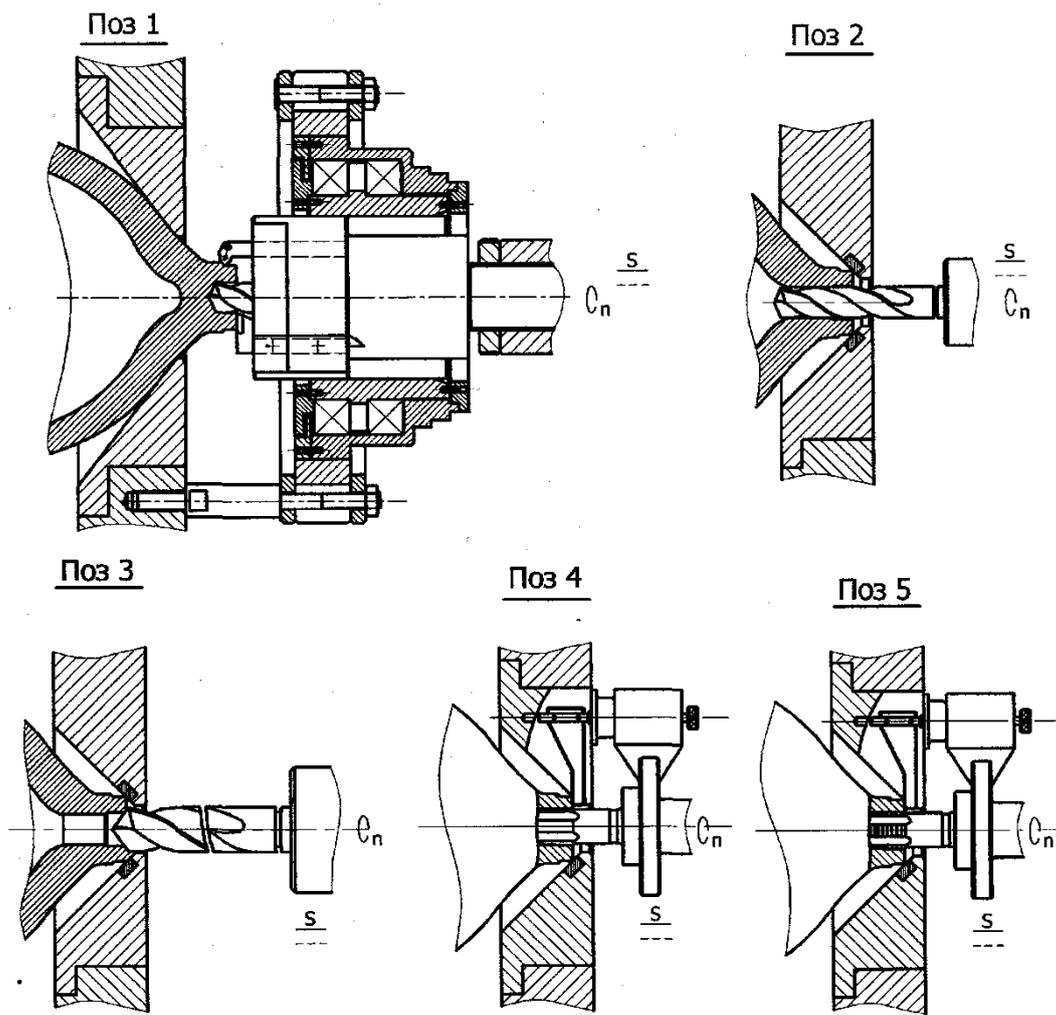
Новый технологический процесс механической обработки резьбового отверстия в горловине баллона
